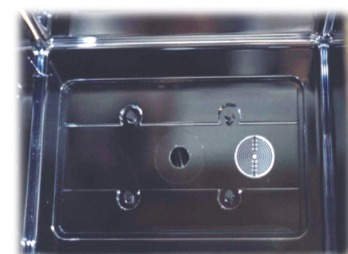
Im Werkzeug eingebauter TMS™-Sensor
